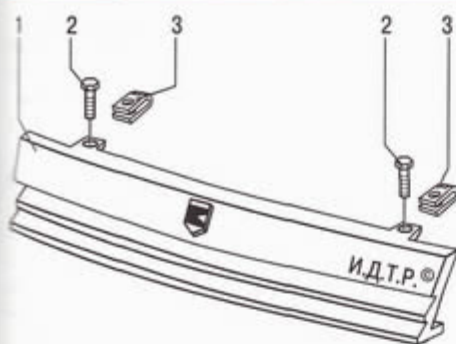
Крепление облицовки радиатора: 1 – облицовка радиатора; 2 – болт; 3 – пластинчатая гайка
